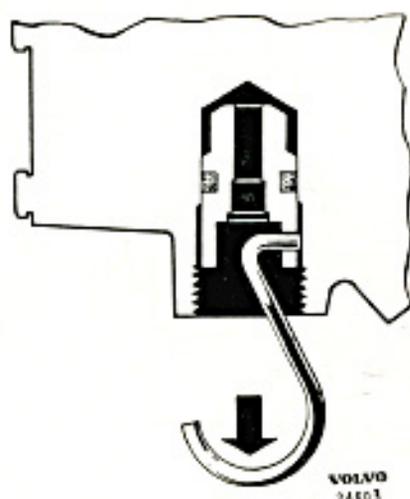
Demontering av ventilsäte, reduceringsventil
